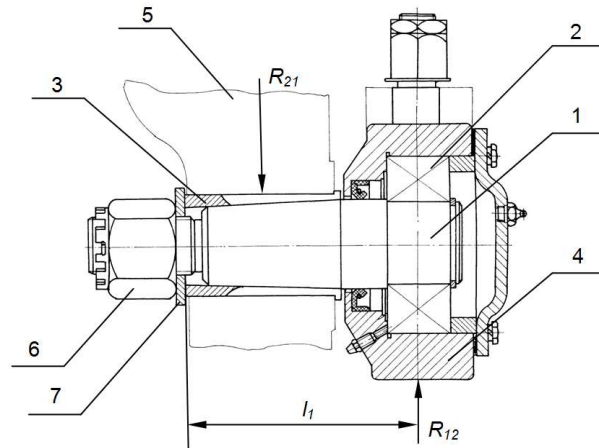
Конструкція вузла з'єднання шатуна з кривошипом
